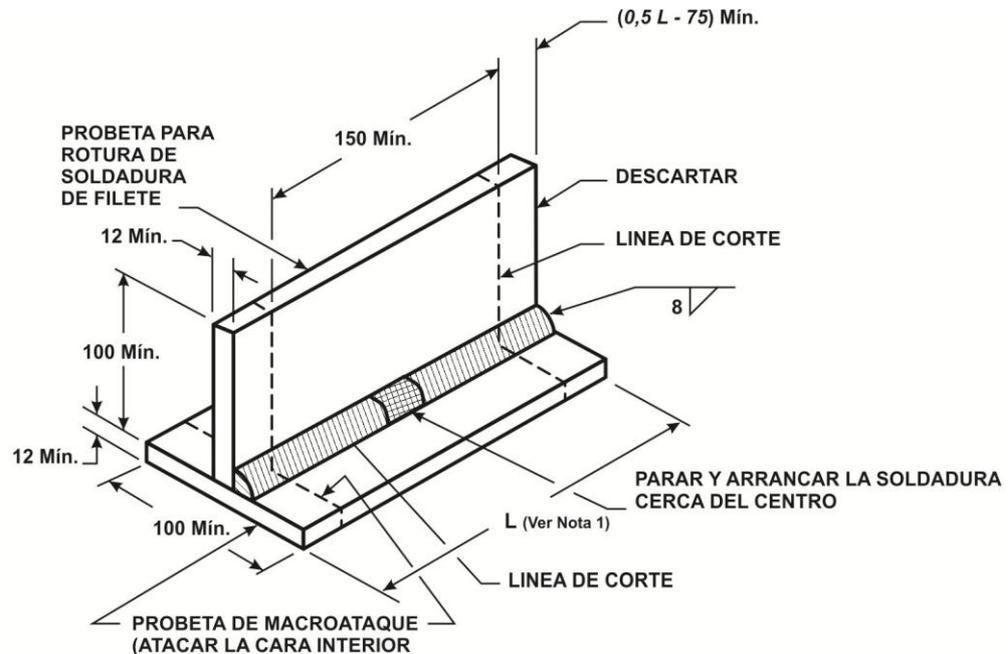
Método de rotura de la probeta – Calificación de soldador punteador.
